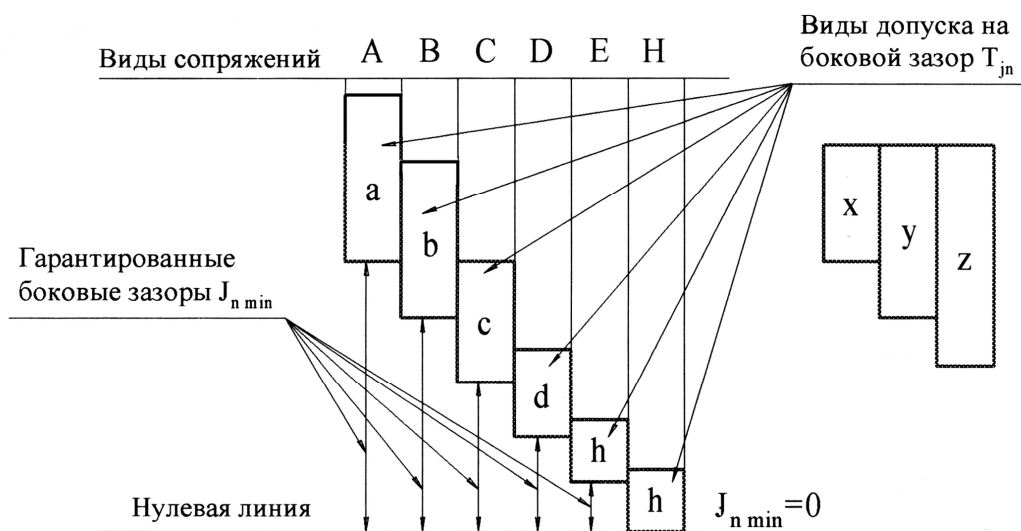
Виды сопряжений и допусков на боковой зазор для передач с модулем $m \geq 1$ мм.
